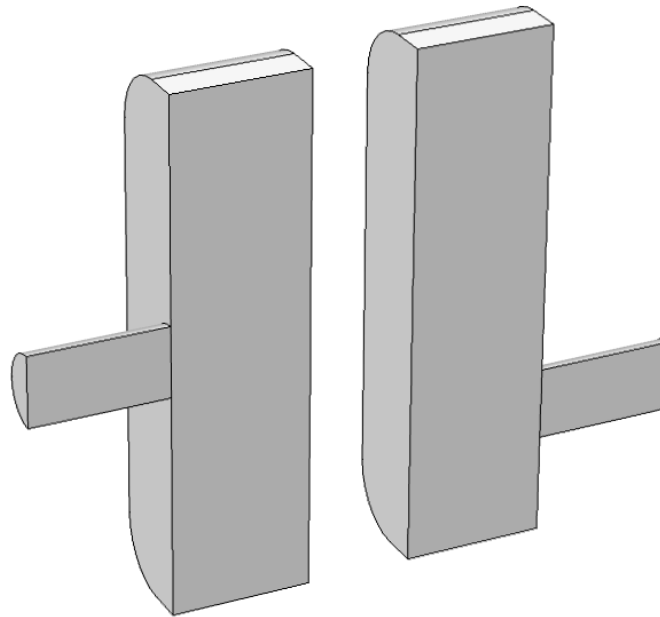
Geometría rectangular con chaflán seccionada por plano vertical
